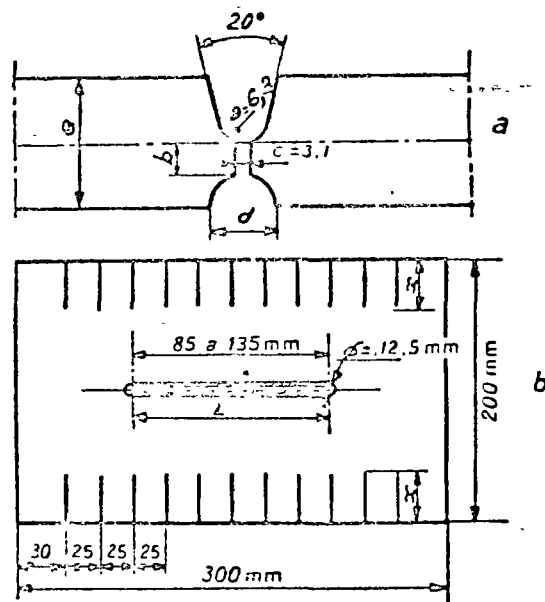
Probeta de la Universidad de LEHIGH.
